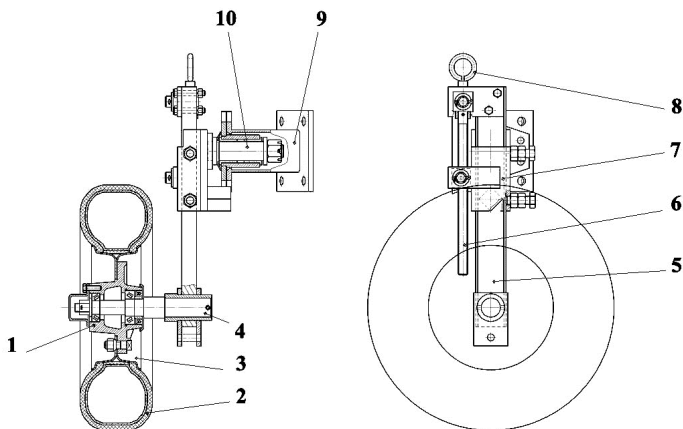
Схемы опорного колеса с механизмом регулировки:
